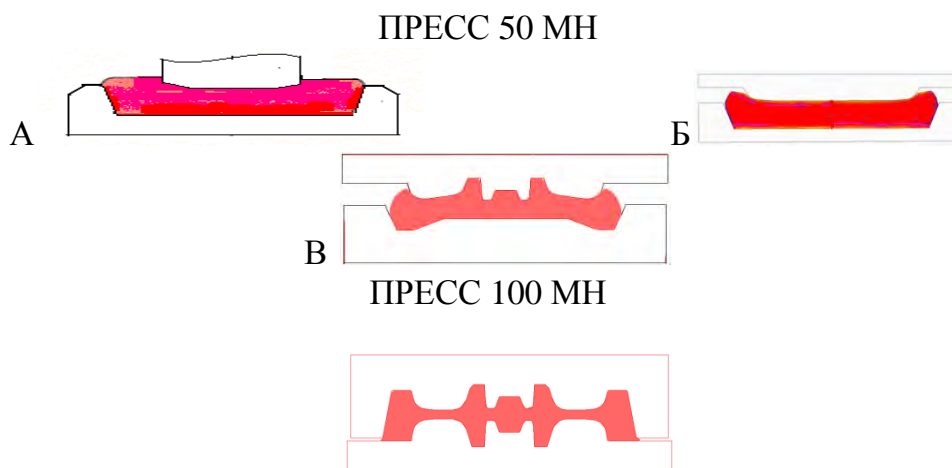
Технологические схемы штамповки заготовок железнодорожных колес: А - штамповка колесной заготовки на формовочном прессе силой 100 МН после предварительной разгонки; Б - разгонка заготовки на прессе силой 50 МН; В - штамповка колесной заготовки на прессе силой 100 МН из поковки
